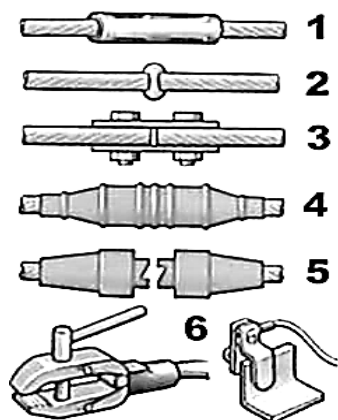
Присоединение сварочного кабеля:
